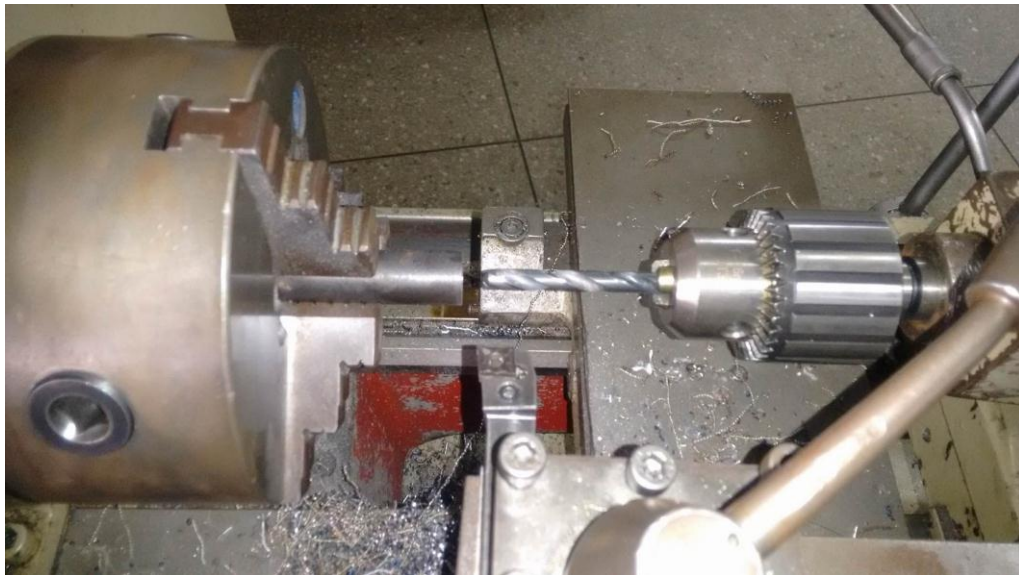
Fabricación del elemento Brida del BlankHolder
